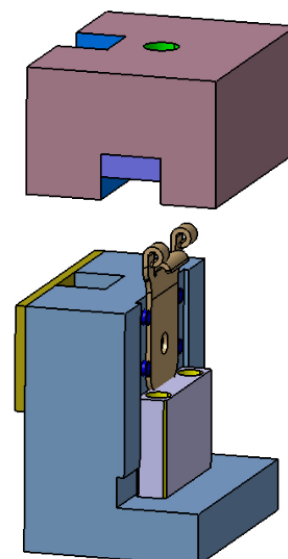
Vizualizace jednoduchého nástroje pro první ohyb [29]
